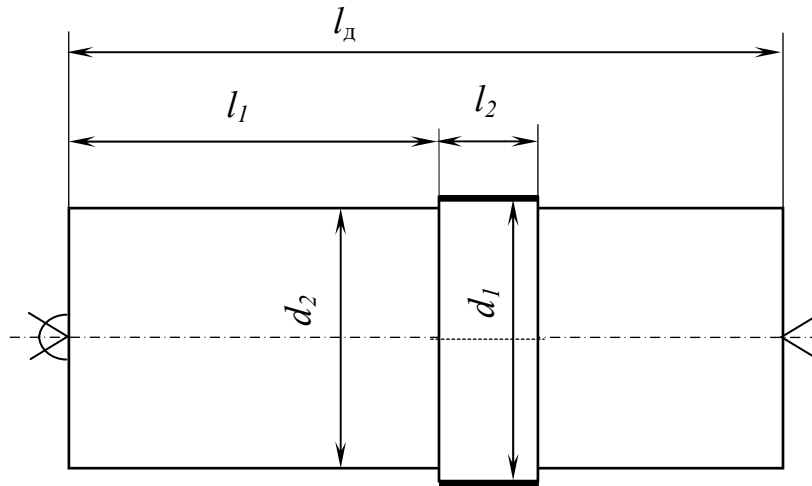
Операційний ескіз до визначення сумарної похибки токарної обробки
